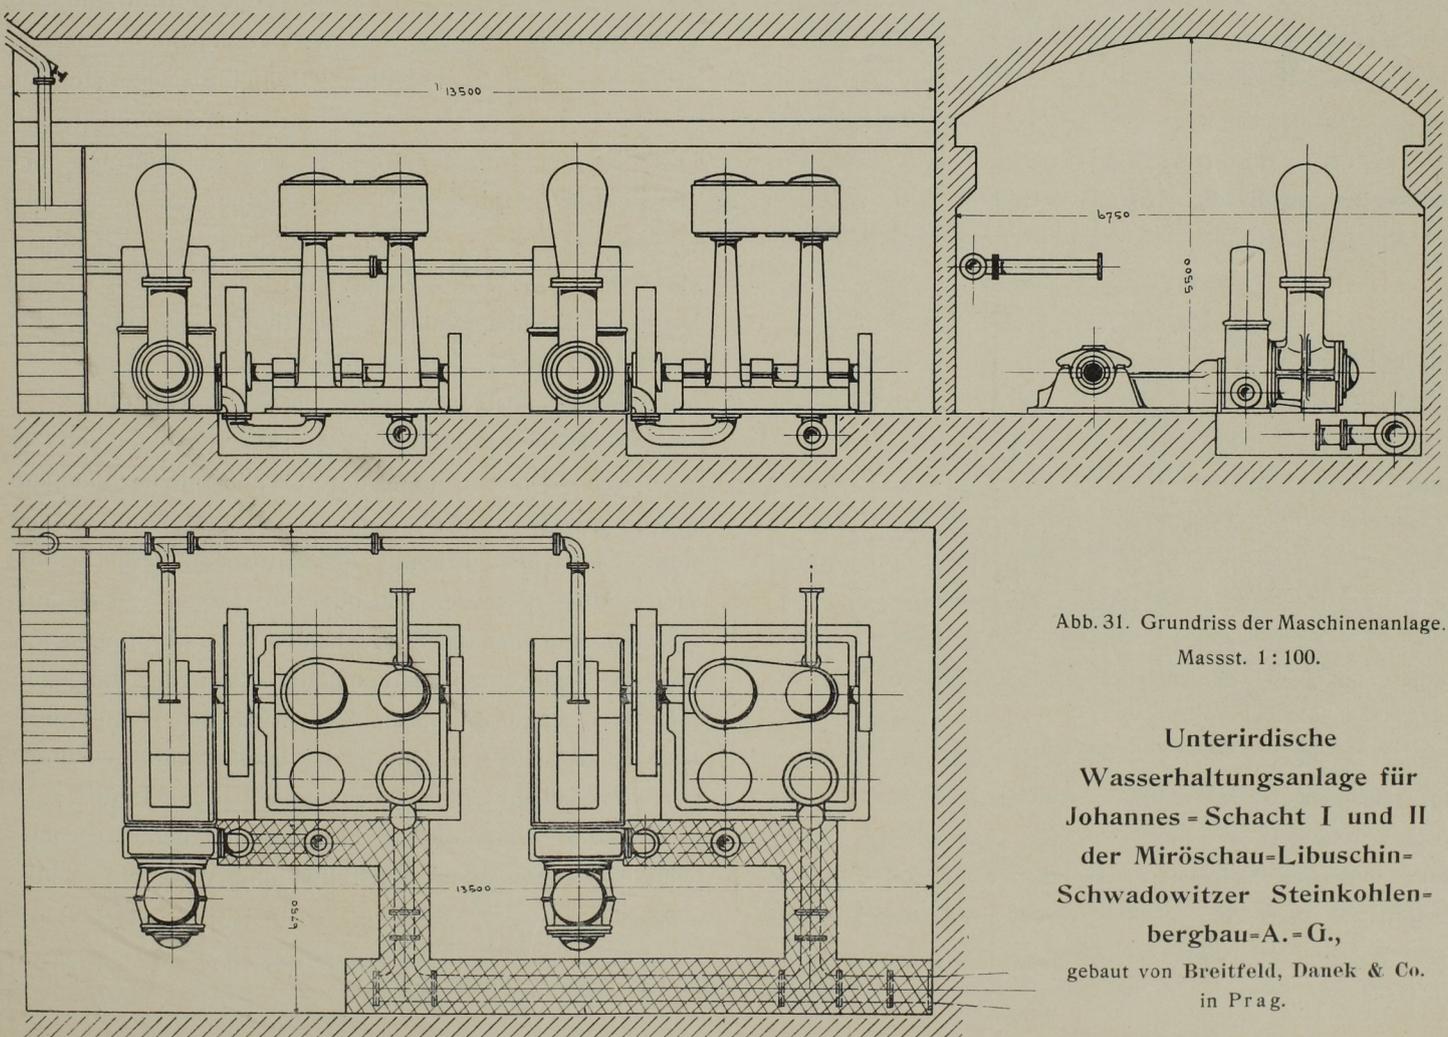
Grundriss der Maschinenanlage. Masst. 1:100.
